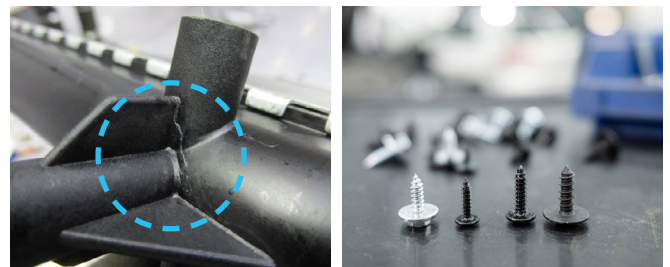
Risse am Kühlmittelkühler durch falsche Schrauben
